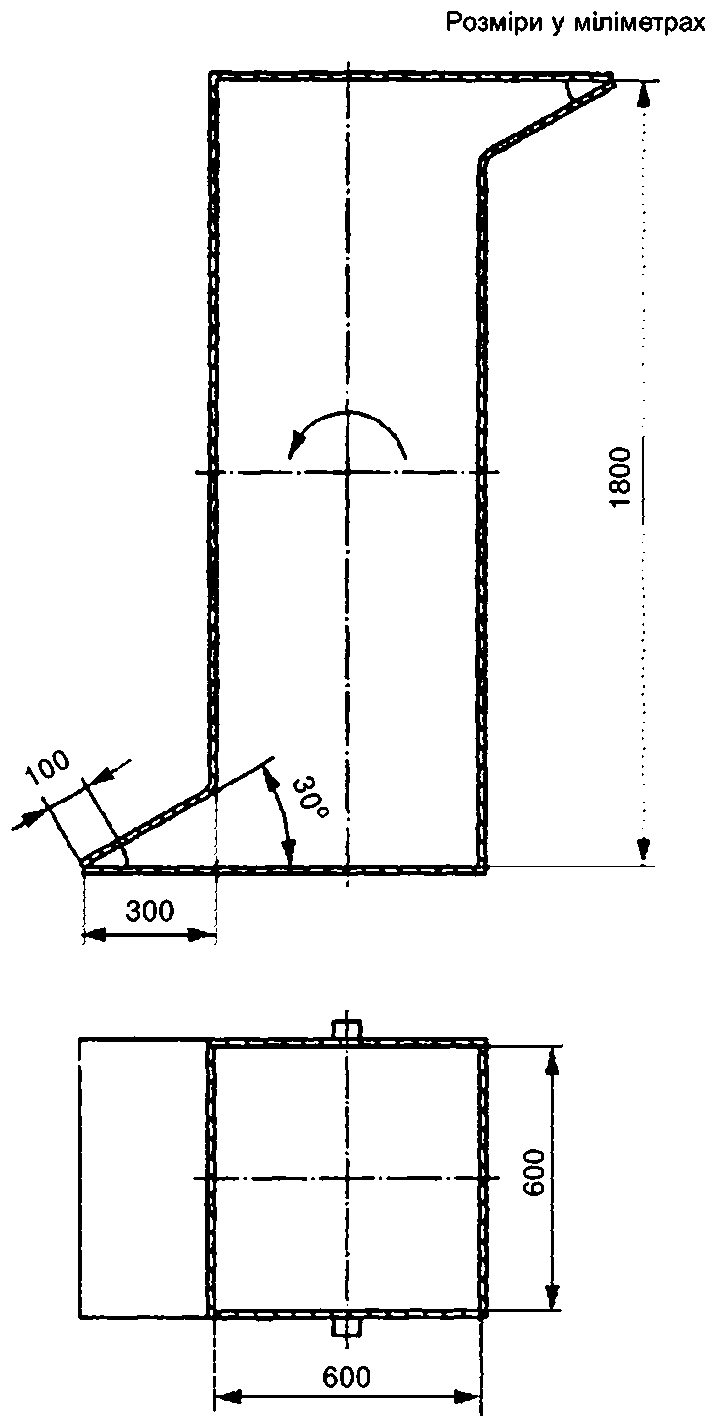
Схема установки для випробовування гідрокостюма на удар під час обертання
